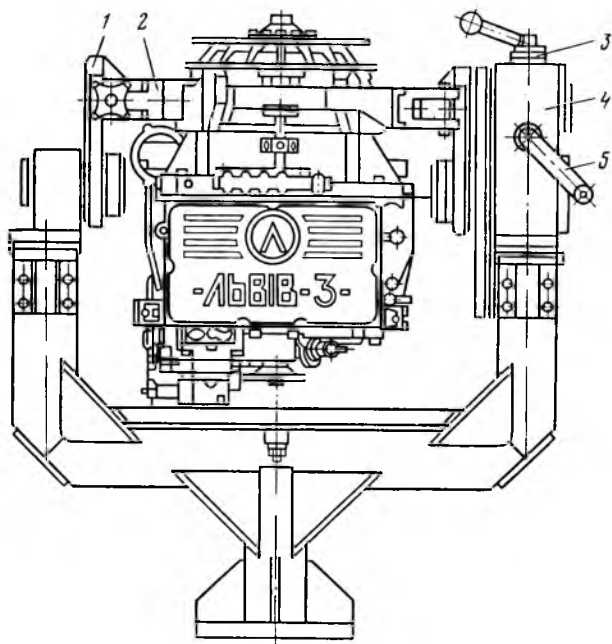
Стенд для ремонта гидромеханической коробки передач:
